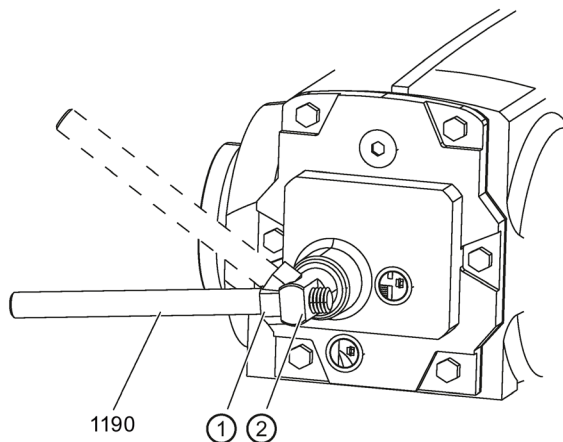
Расположение, обеспечивающее минимальную нагрузку на вал и подшипники
